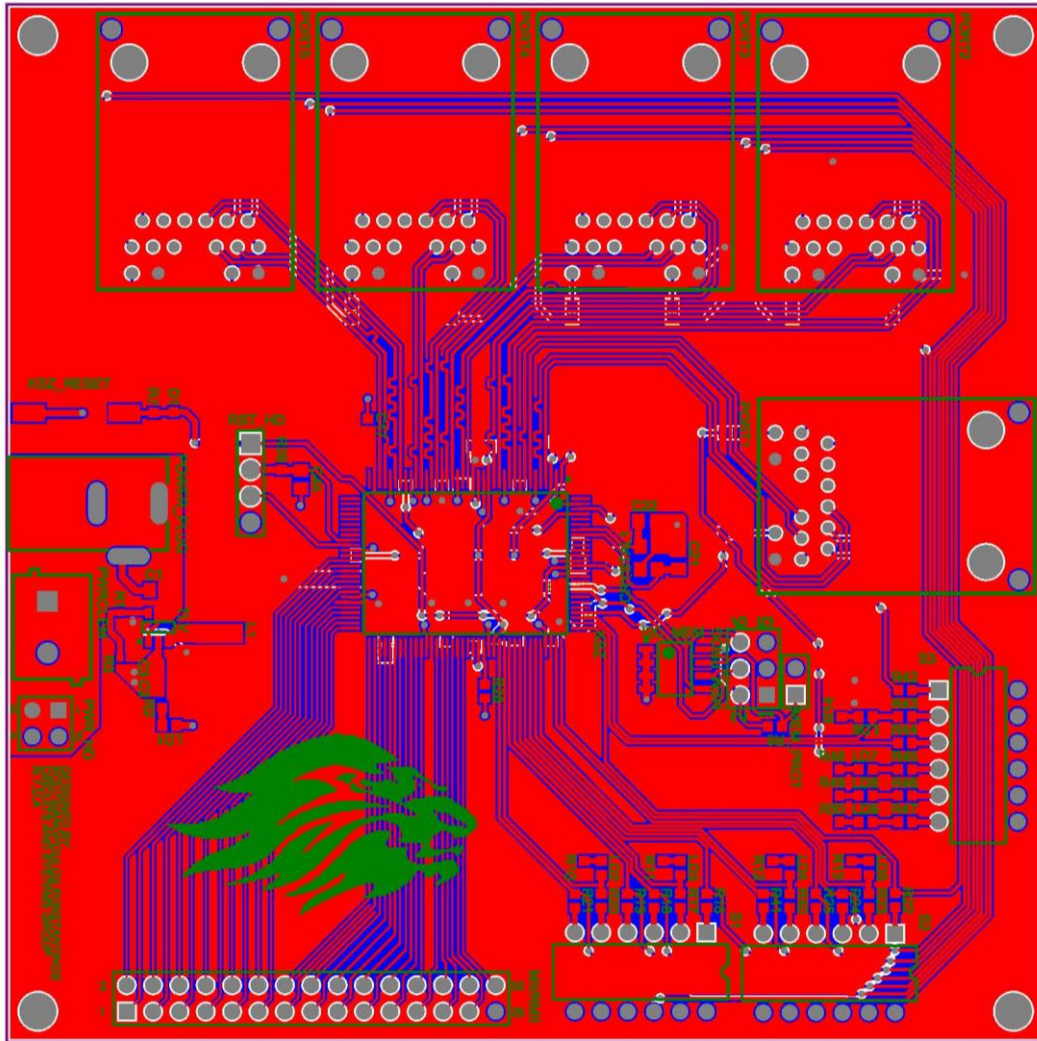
Τελικό PCB Layout της πλακέτας VGA->USB
